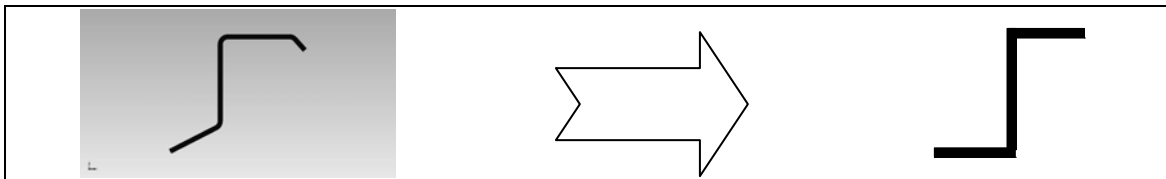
Perfil original e considerado da travessa da zona dos eixos
